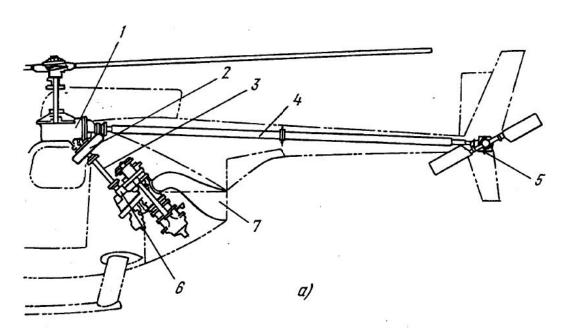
Компоновка трансмиссии вертолета МИ-8: 1 — вал привода вентилятора; 2 — ГР; 3 — тормоз НВ; 4 — вал РВ; 5 — промежуточный редуктор; 6 — промежуточный вал; 7 — редуктор РВ
